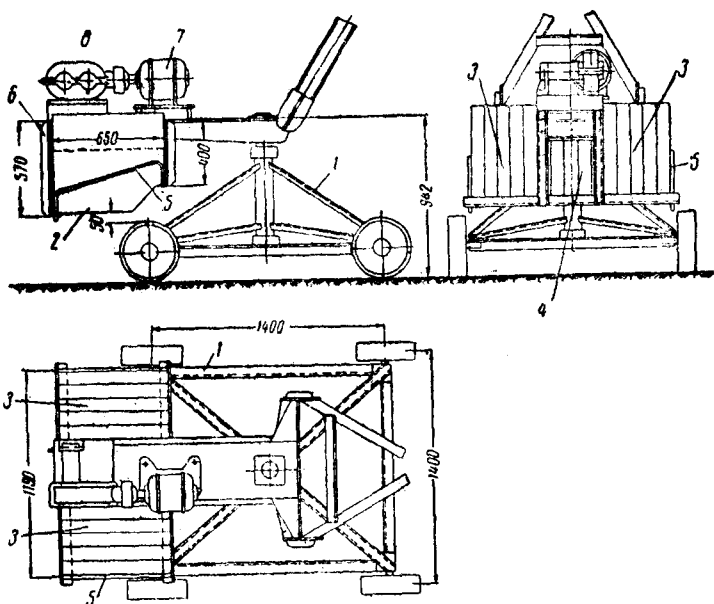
配置有钢筋混凝土块平衡锤的“先锋牌”起重机行动小車
